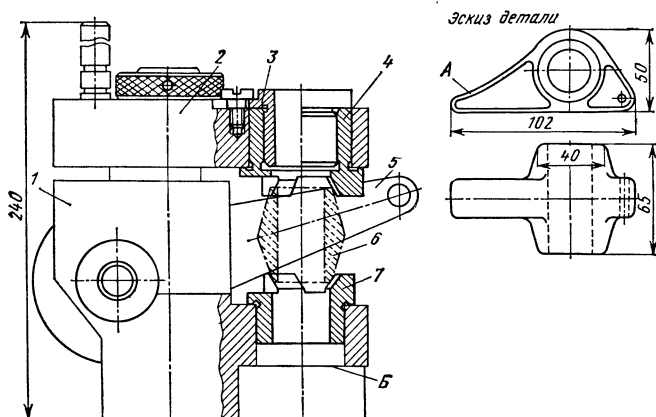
Наладка к скальчатому кондуктору для сверления отверстия в центре бобышки рычага
